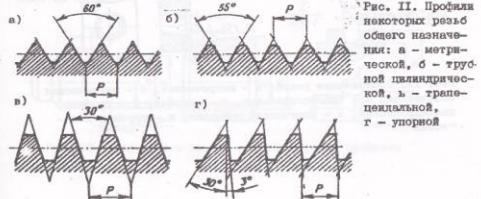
Рис. II. Профили некоторых резьб общего назначения: а - метрической, б - трубной цилиндрической, в - трапециoidalной, г - упорной
